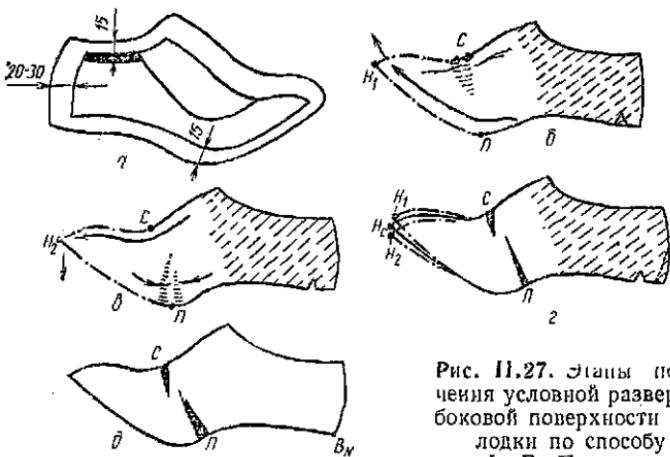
Этапы получения условной развертки боковой поверхности колодки по способу Ф. В. Пешикова
